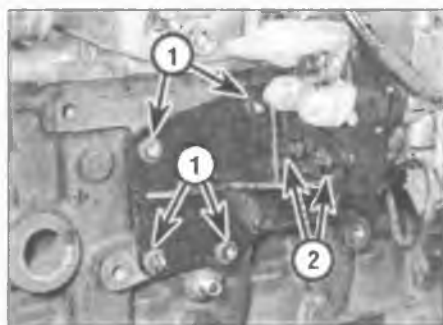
,а. Выверните болты (1), отверните гайки и выверните болты (2), ...
